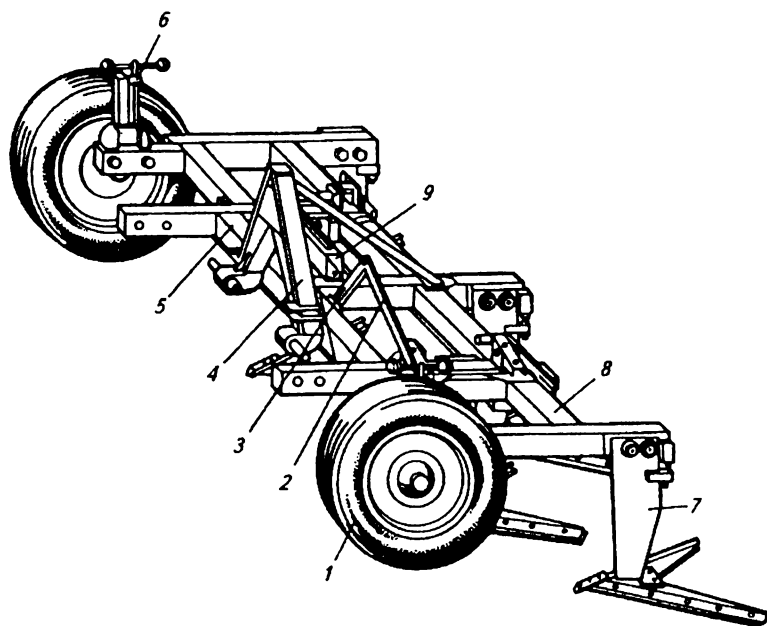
Широкозахватный культиватор-плоскорез КПШ-5: 1 — пневматическое колесо; 2 — тяга; 3 — рычаг; 4 — замок; 5 — центральная рама; 6 — механизм опорного колеса; 7 — рабочий орган; 8 — боковая рама; 9 — гидроцилиндр
